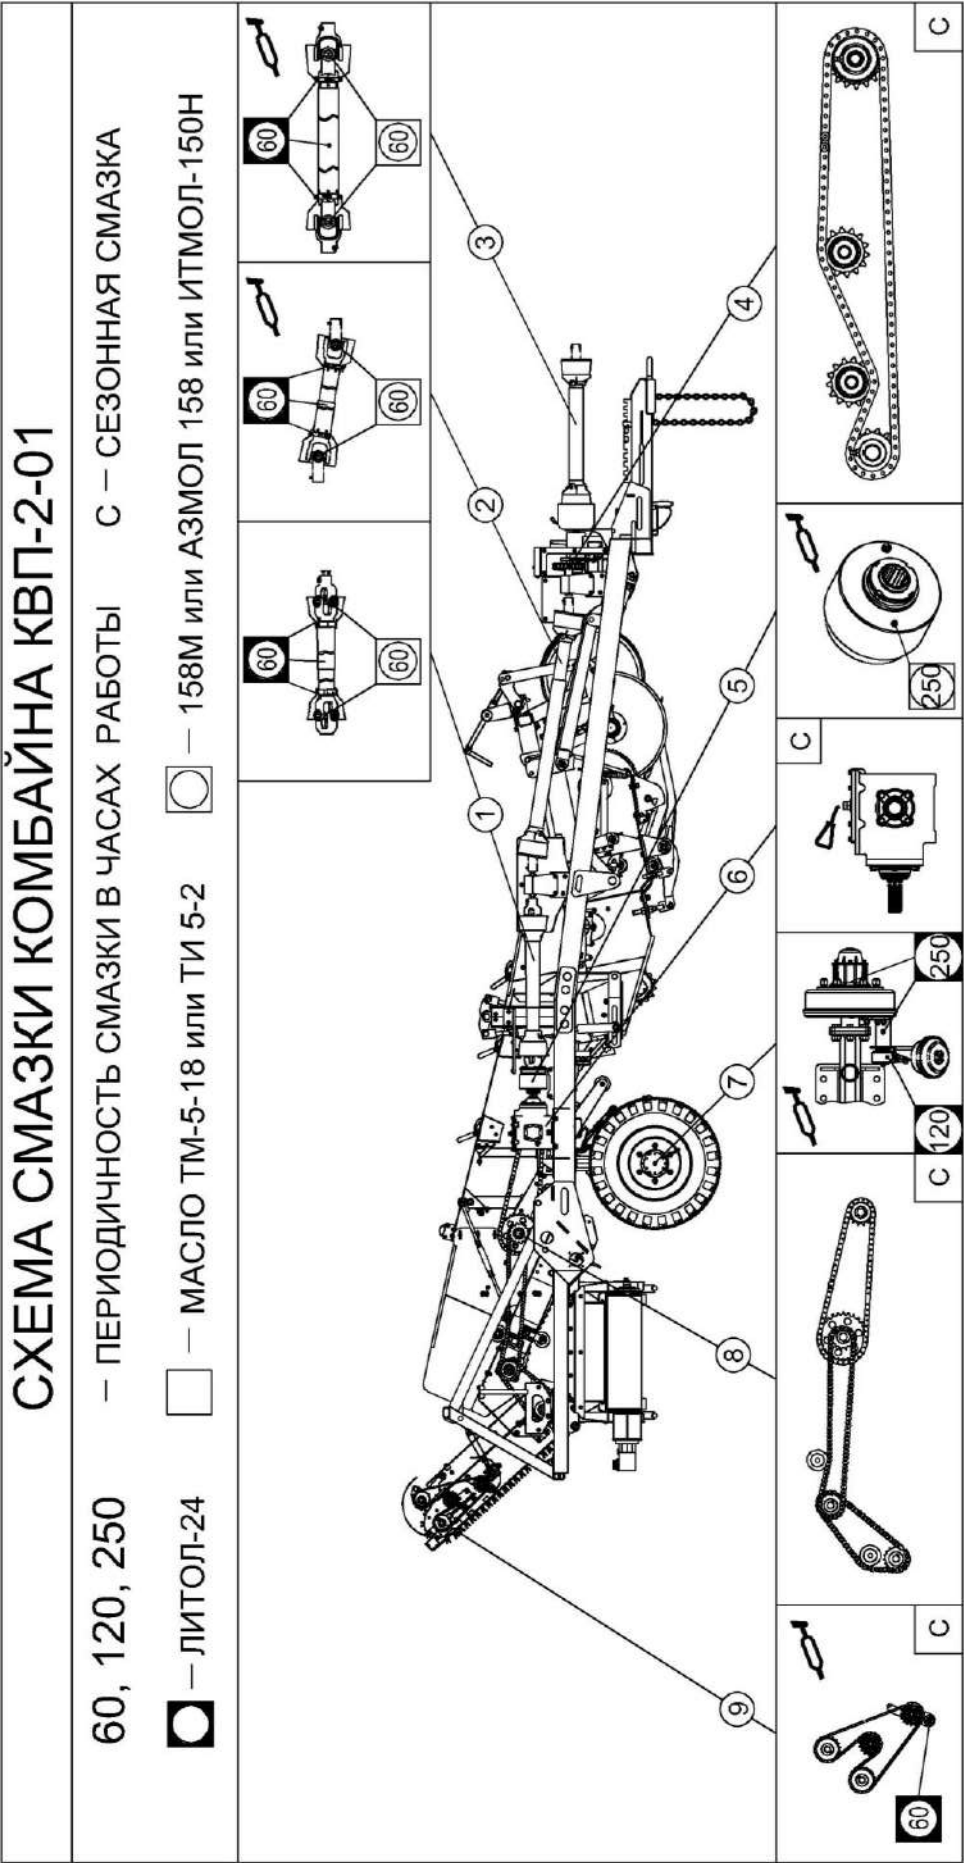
Схема смазки картофелекопателя КВП-2-01
